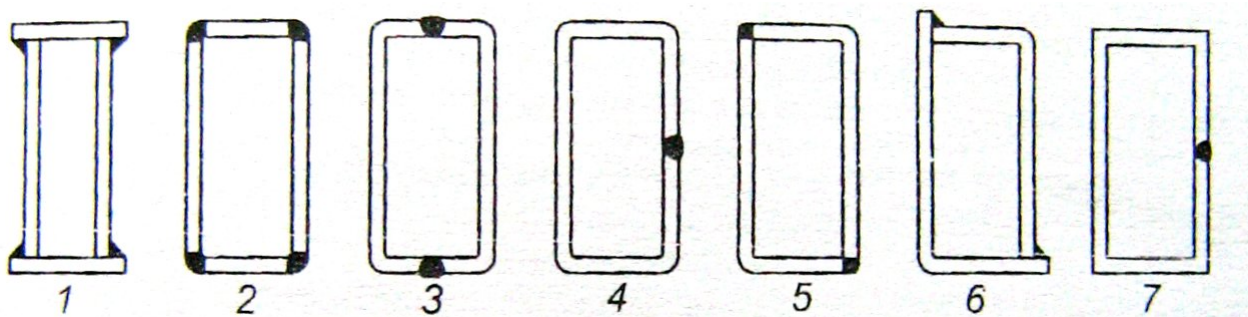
варіанти зварювання балки коробчастого перерізу
